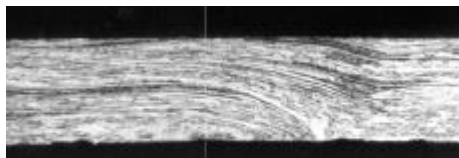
Gefügestruktur einer Hammerschweißung FKS 16Pt
